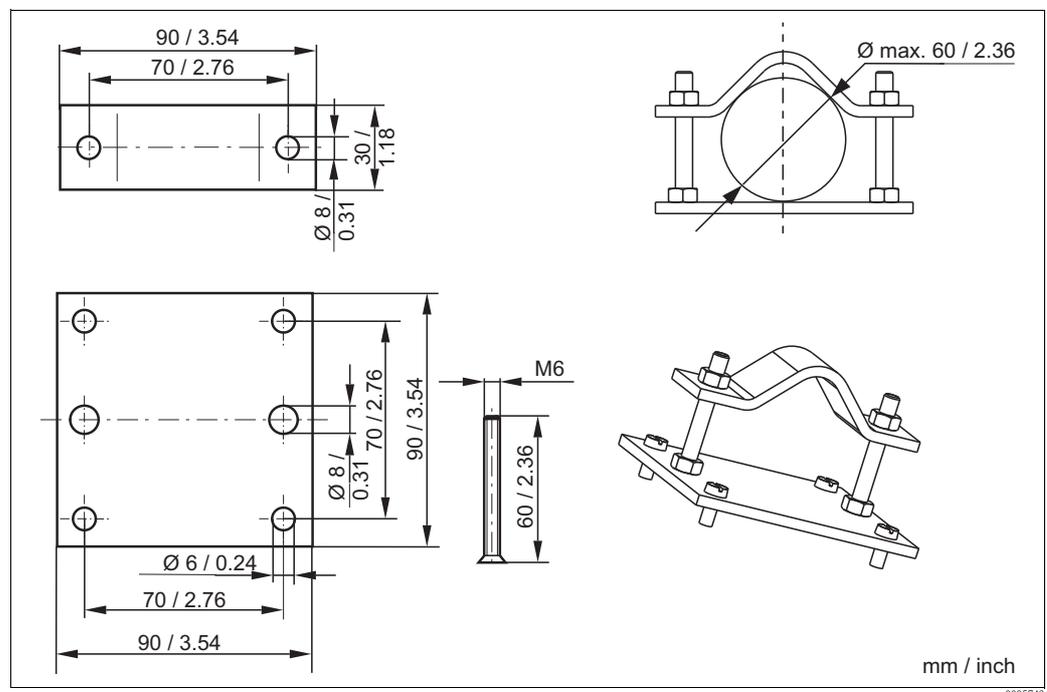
Kit de montage pour la fixation sur tube ou mât
